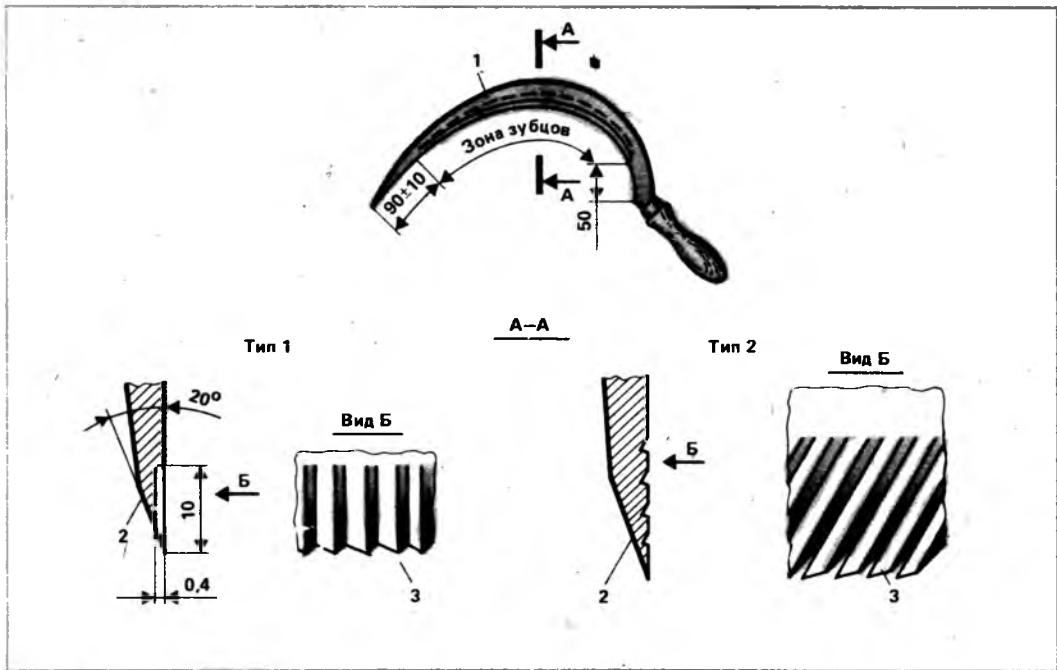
Разновидности режущей кромки серпа: 1 — полотно ножа; 2 — фаска; 3 — зубцы
